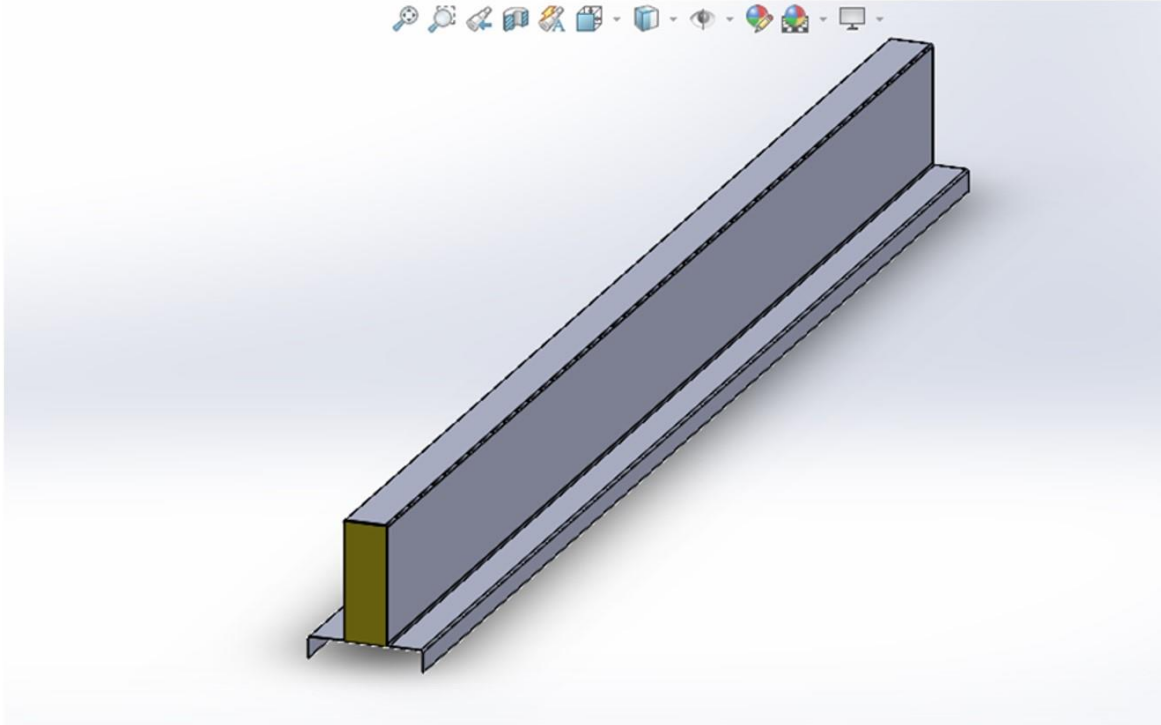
CAD de estructura final de lámina galvanizada y fibra aislante
